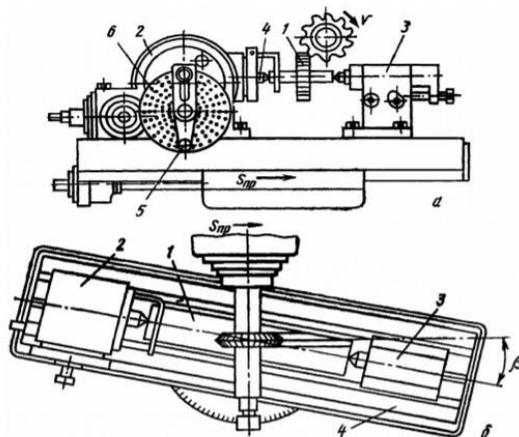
Обработка заготовок с помощью делительной головки
